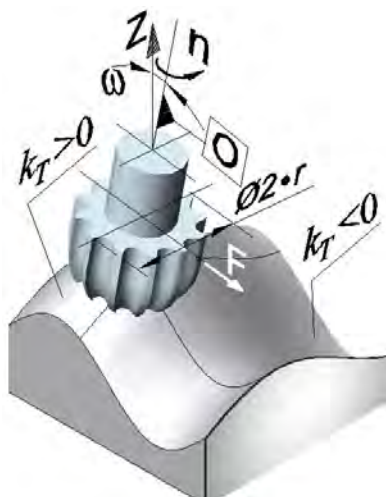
Схема фрезерования сложно – профильной поверхности
